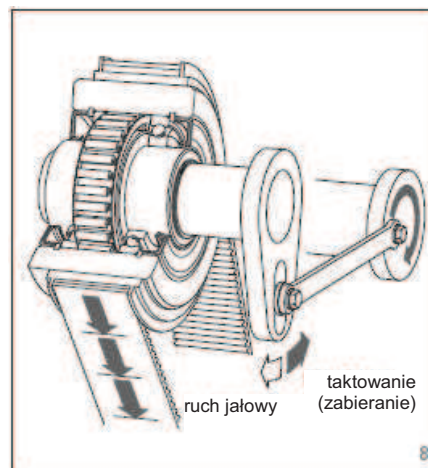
przedstawia wolnobieg rozłączający, w którym w stanie napędzania przepływ siły odbywa się z pierścienia zewnętrznego na wewnętrzny, natomiast na biegu jałowym pierścień wewnętrzny o wyższych obrotach wyprzedza pierścień zewnętrzny.
